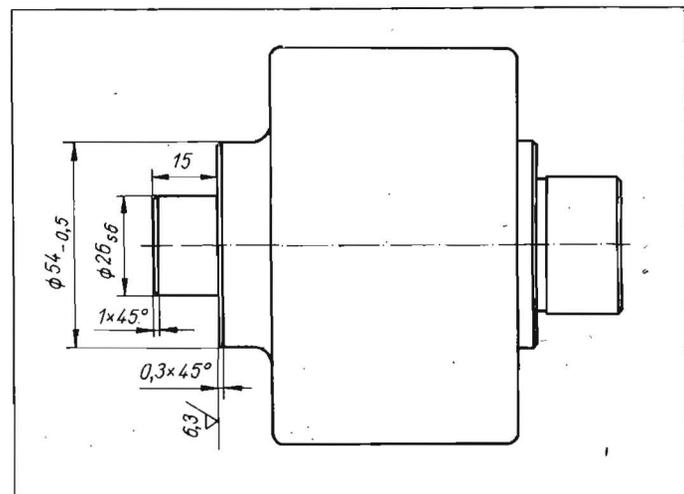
Neugefertigter Rohling als Anschweißteil für Planetenritzel [10]
